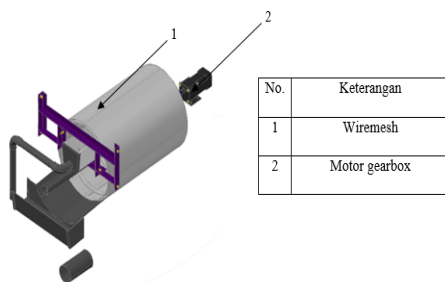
4 Mesin *Rotary Drum Filter 3M
